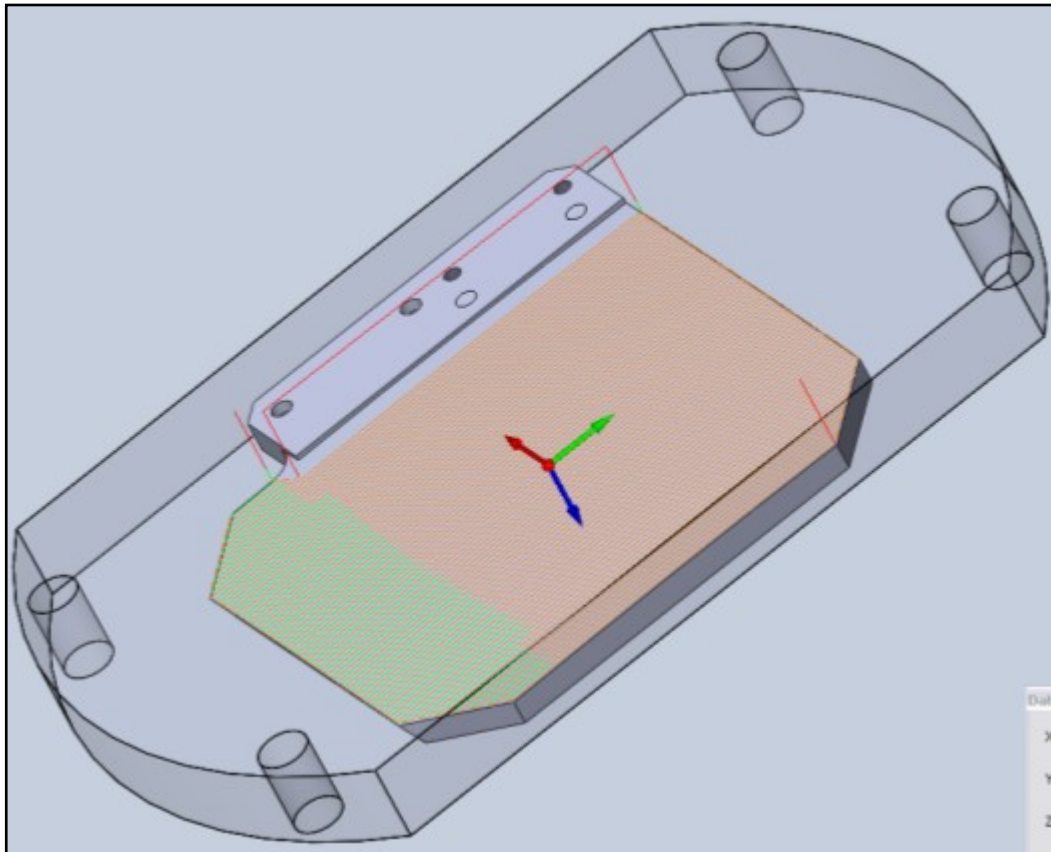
Hotové zrcadlo po frézování po frézování na čisto (po odpíchnutí); č. op. 180.
